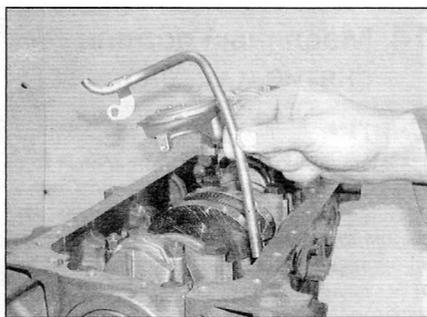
, б. ...затем снимите направляющую трубку с блока цилиндров (показано на снятом двигателе)
